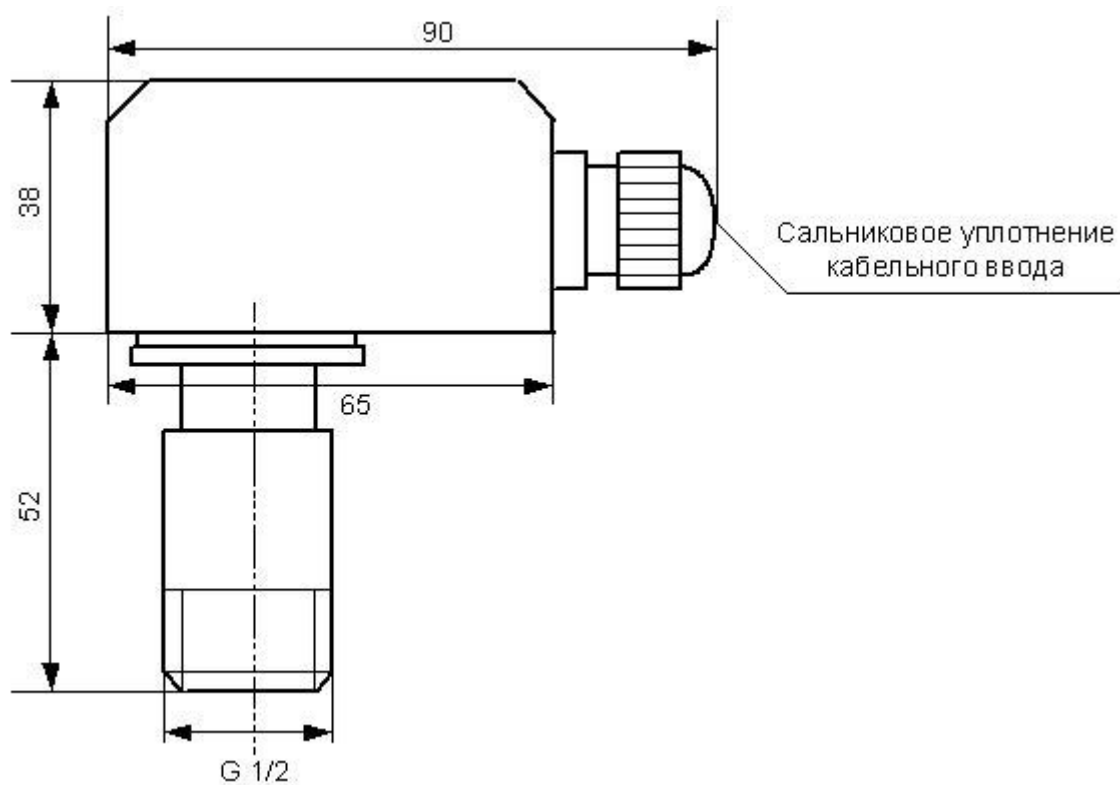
Внешний вид и габаритные размеры датчика давления
